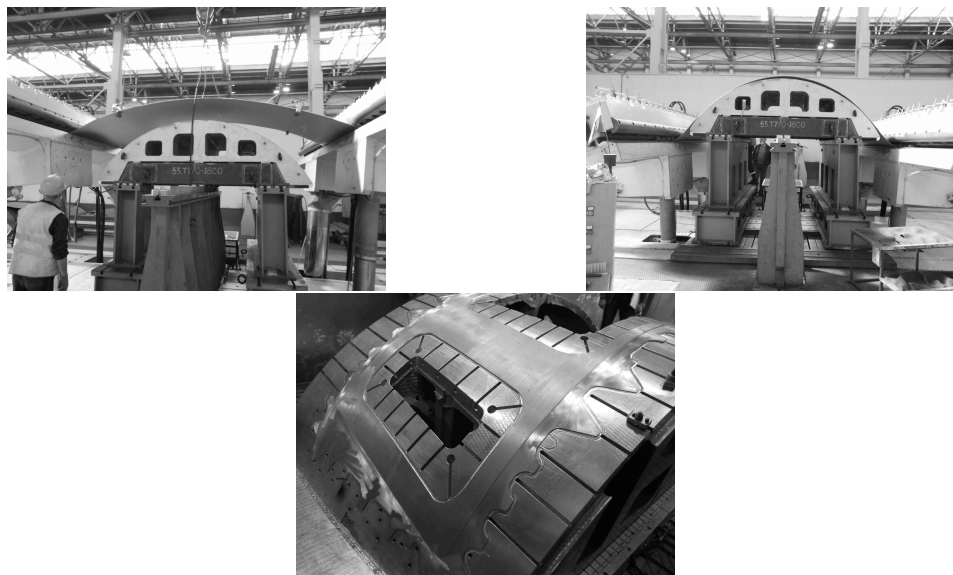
Результат отработки технологии обтяжки крупногабаритной заготовки и механической обработки окантовки двери.
